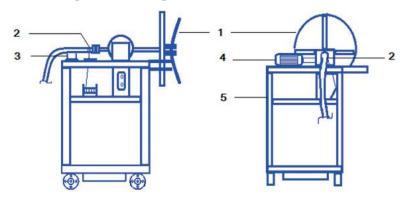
Рабочий эскиз комбинированного станка для технического обслуживания и ремонта напорных пожарных рукавов:
